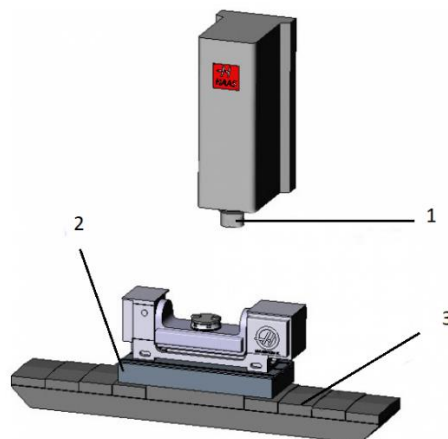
Стіл та шпindel ь фрезерного верстату з ЧПУ:
